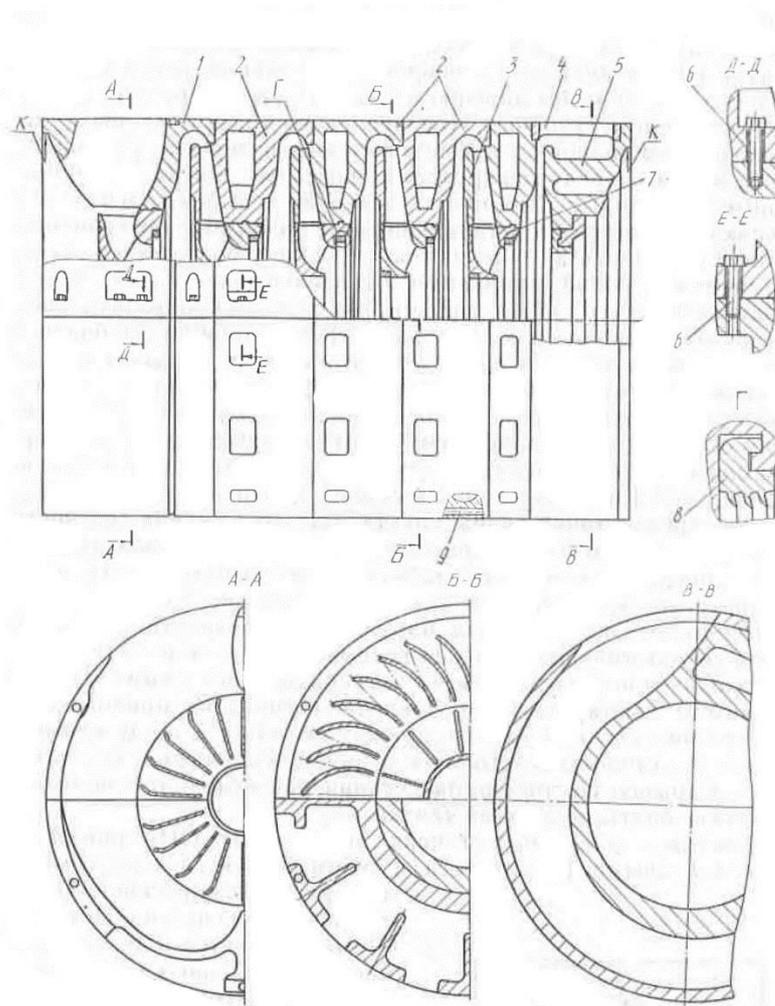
Набор диафрагм компрессора с вертикальным соединением. 1 - Всасывающая камера; 2 – промежуточная мембрана; 3 - внутренняя перегородка с НЕЙ; 4 - распорное кольцо; 5 – концевая часть мембраны со шнеком; 6 - болты, сваривающие половинки мембраны; 7 - лопасть; 8 - лабиринтная втулка; 9 - натяжные штифты
